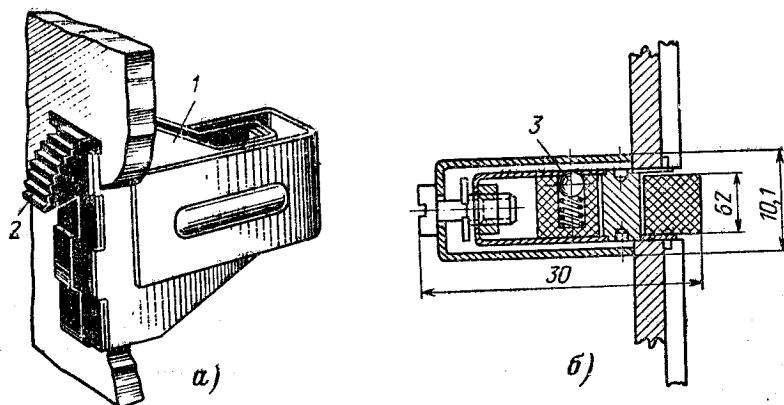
Поворотный символ разъединителя типа СР-2 (используется при двойной системе шин).
